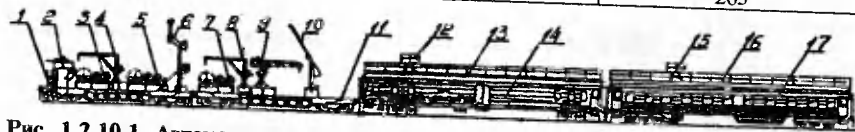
Автоматизированный поезд для ремонта контактной сети РП-1: 1, 11 — платформа; 2 — кабина управления; 3 — блок подачи несущего троса; 4, 8 — кран-балка; 5, 7 — блок подачи контактного провода; 6 — рама; 9 — подъемник гидравлический; 10 — стрела-манипулятор; 12, 15 — тележка монтажная; 13, 16 — неизолированная рабочая площадка; 14 — вагон-склад; 17 — вагон-салон
